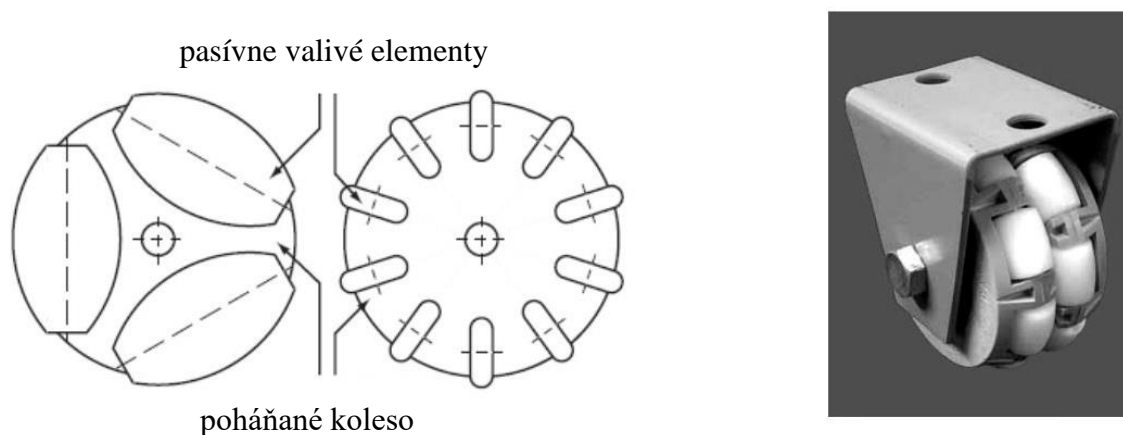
Pohonná jednotka jednokolesového robota „CMU Ballbot“ [5]
